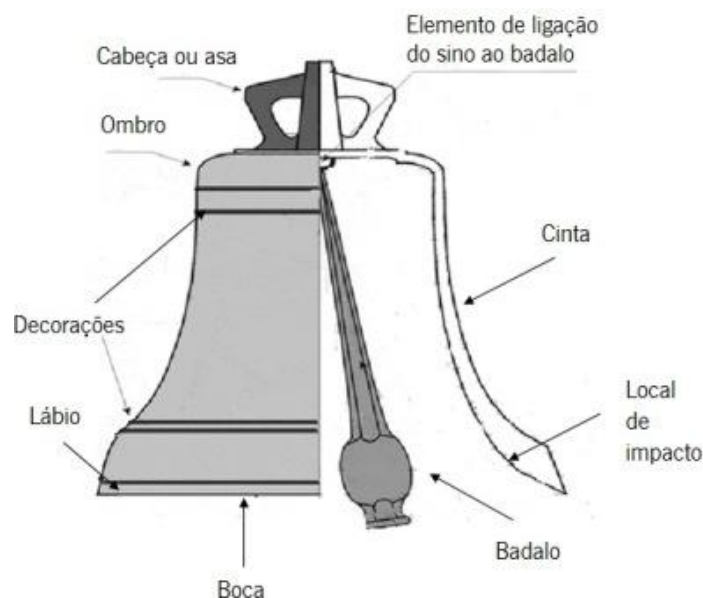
Partes constituintes de um sino [adaptado de 16].
